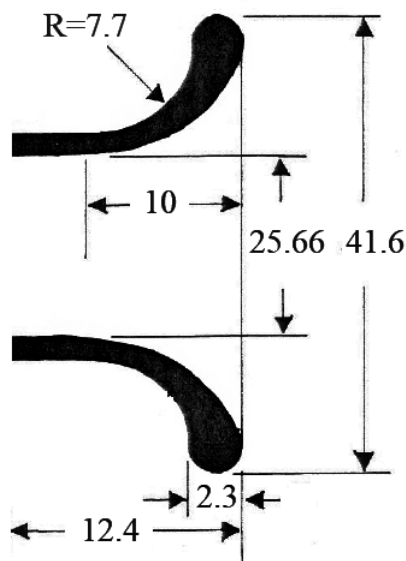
Géométrie et dimensions (en mm) du déflecteur
